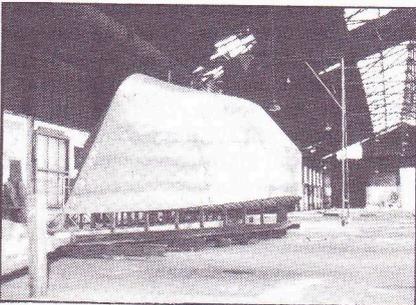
Un 8 mètres acier en construction amateur (Photo M. Portier, constructeur amateur).
